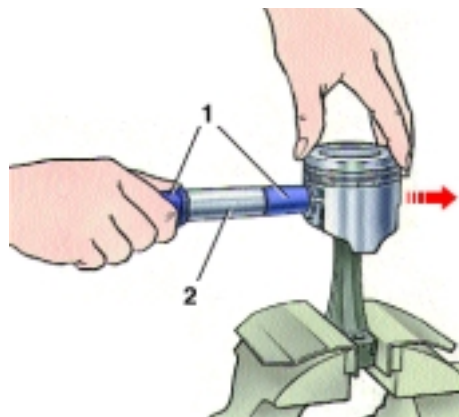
Запрессовка поршневого пальца в верхнюю головку шатуна двигателя мод. 2106-70: 1 – приспособление; 2 – поршневой палец. Поршень должен опираться на головку шатуна в направлении, указанном стрелкой
